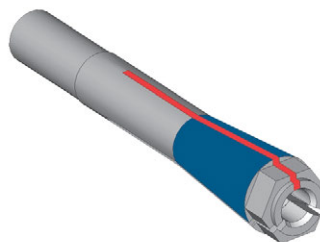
ENGRASAR LA PINZA DE SUJECIÓN; LA SUPERFICIE A LA QUE SE DEBE APLICAR GRASA APARECE MARCADA EN AZUL; LA RANURA QUE NO DEBE ENGRASARSE APARECE MARCADA EN ROJO
